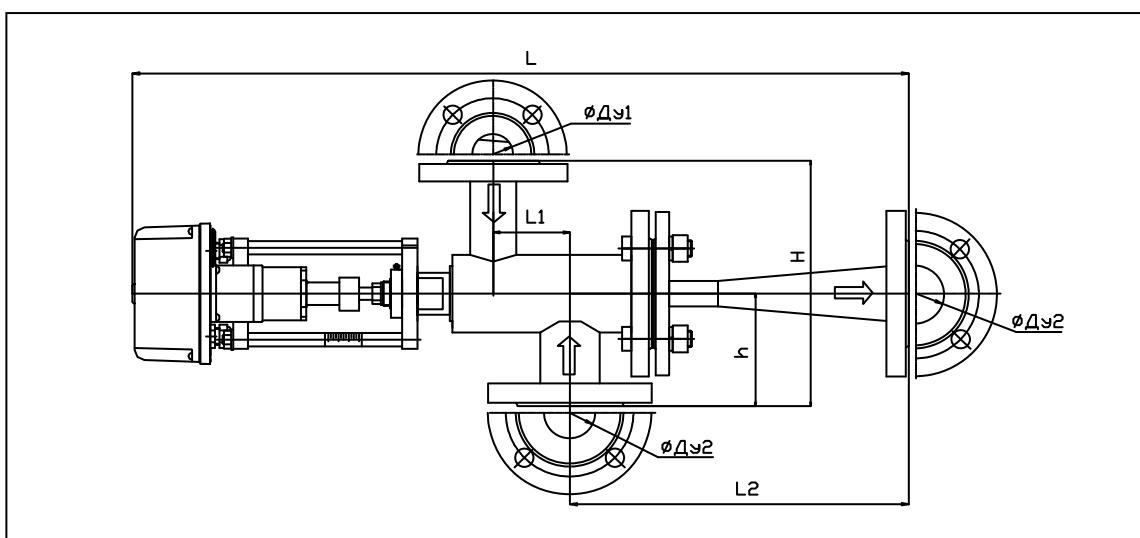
Габаритные и установочные размеры регулирующих гидроэлеваторов РГ (40с941нж)
